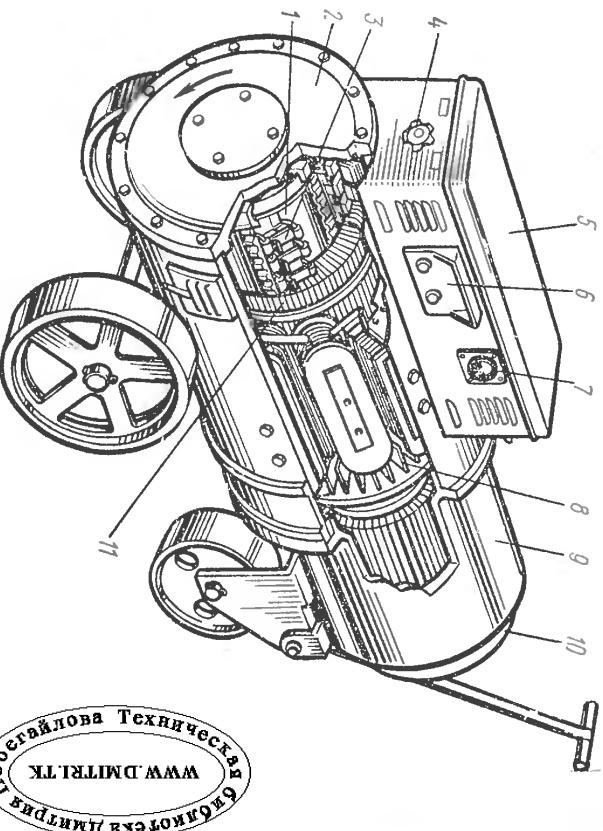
Сварочный преобразователь ПСТ-500-1:
